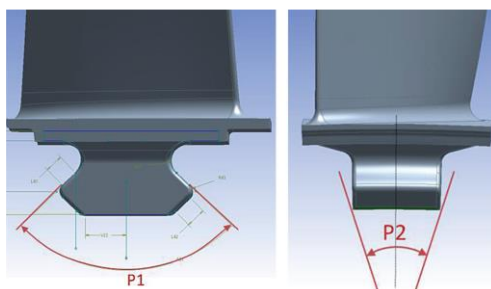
Model parametryczny sekcji wieńca wirnikowego w konfiguracji integralnej
